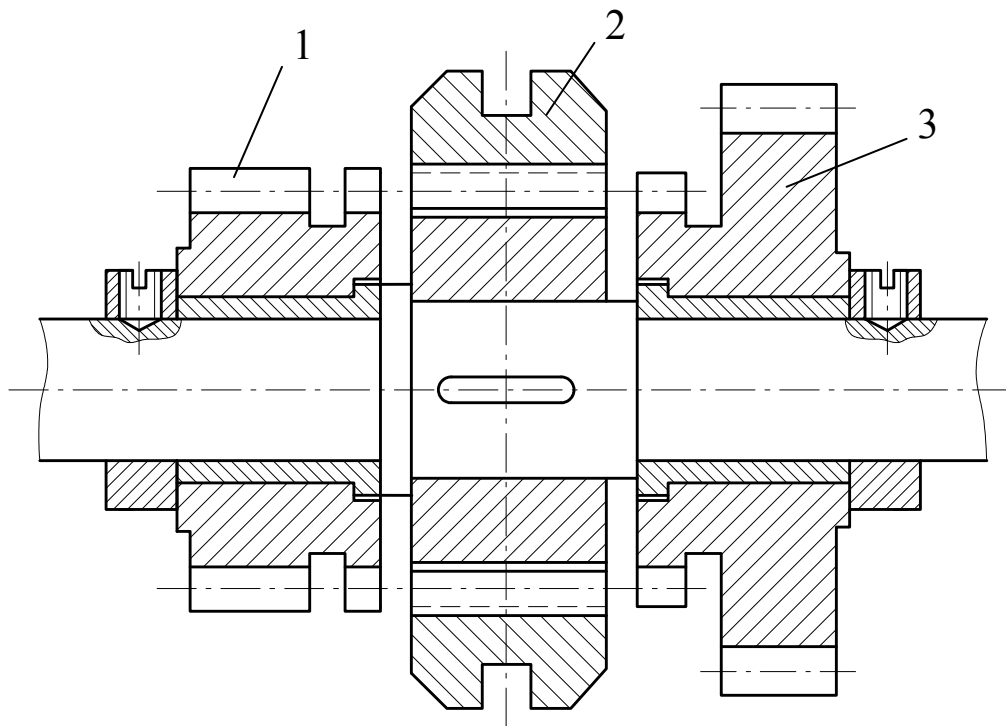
Муфта зубчаста зчіпна з зовнішньою обоймою
